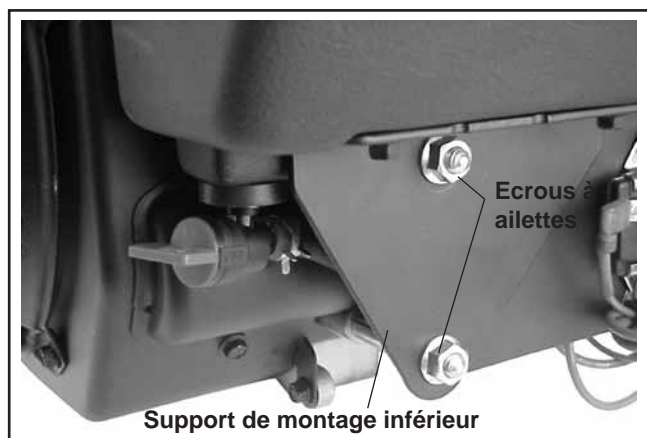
Installation des écrous de montage inférieurs du réservoir de carburant.
